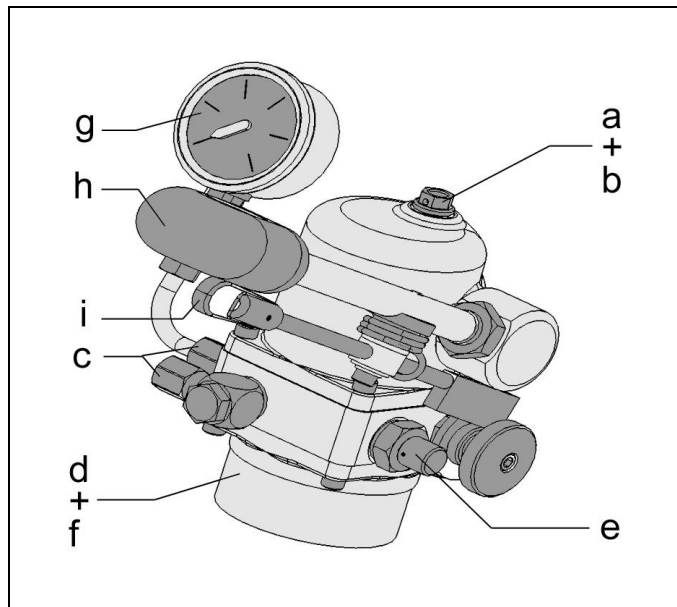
Vue d'ensemble des composants (figure de principe 8804, 8805, 8808, 8816)
